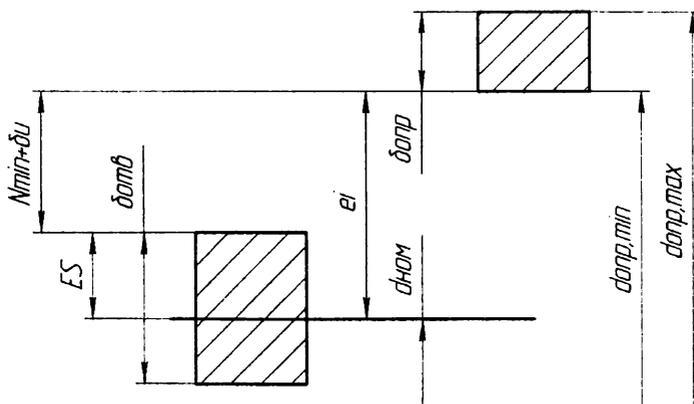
Схема взаимного расположения полей допусков оправки и заготовки
